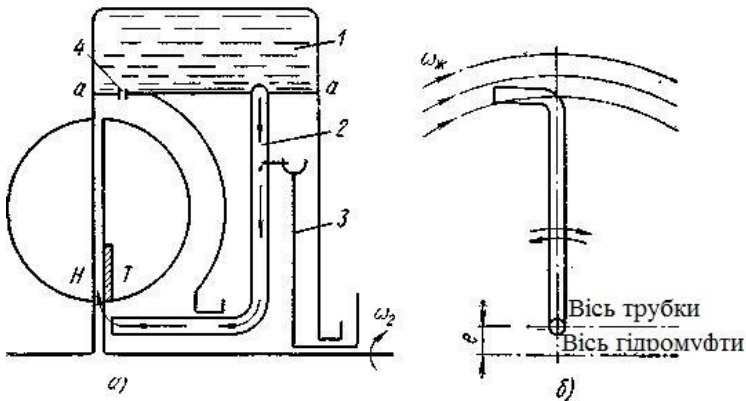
Гідромуфта з поворотною черпаковою трубкою та обертовим резервуаром:
